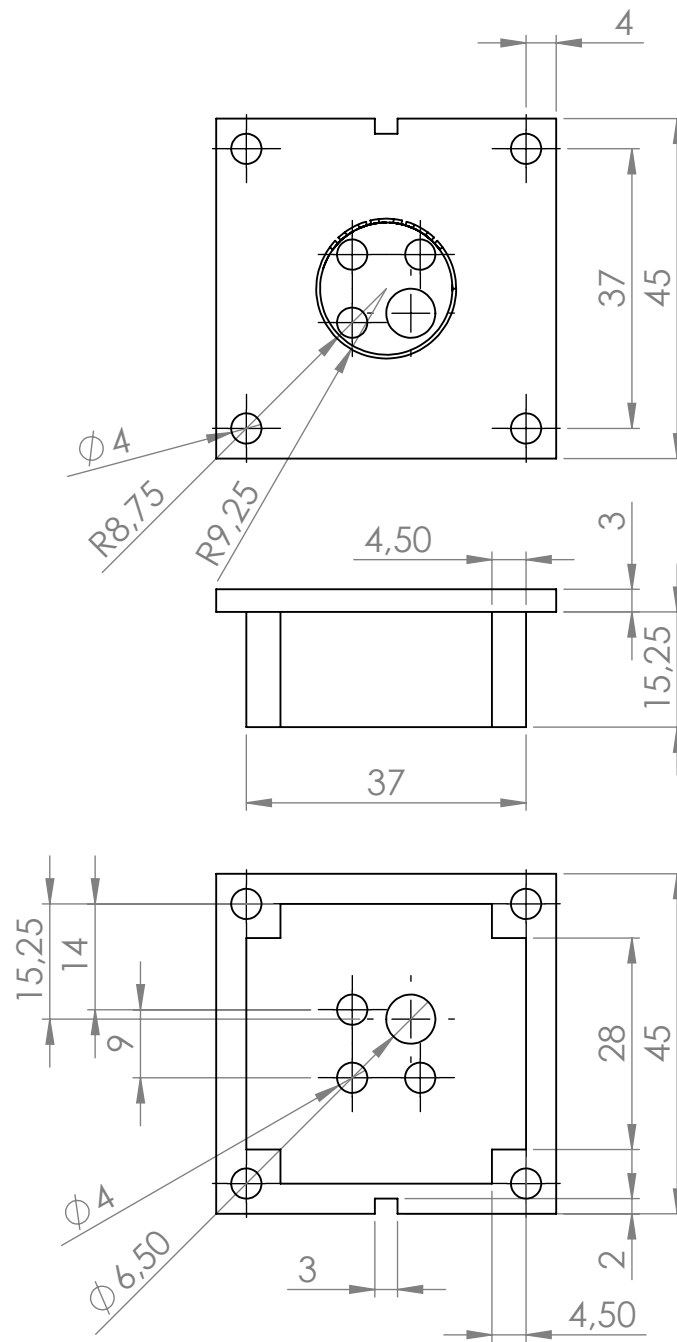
Diseño del molde para enmallado interno del *Robot Tilt* parte B
